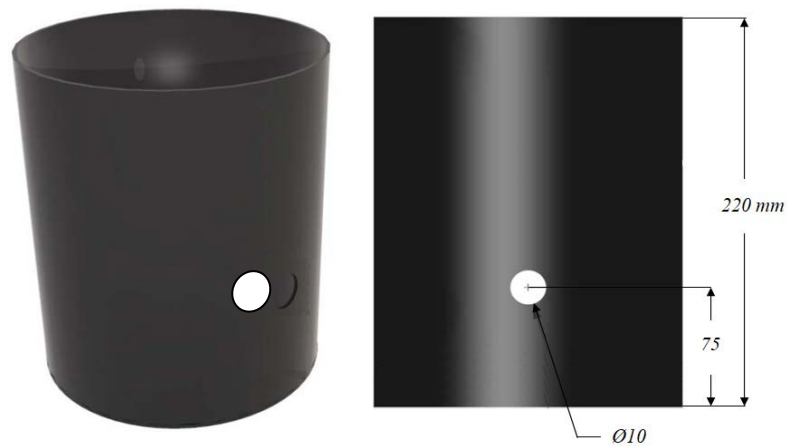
Moule pour éprouvettes en béton armé (essai de corrosion)
